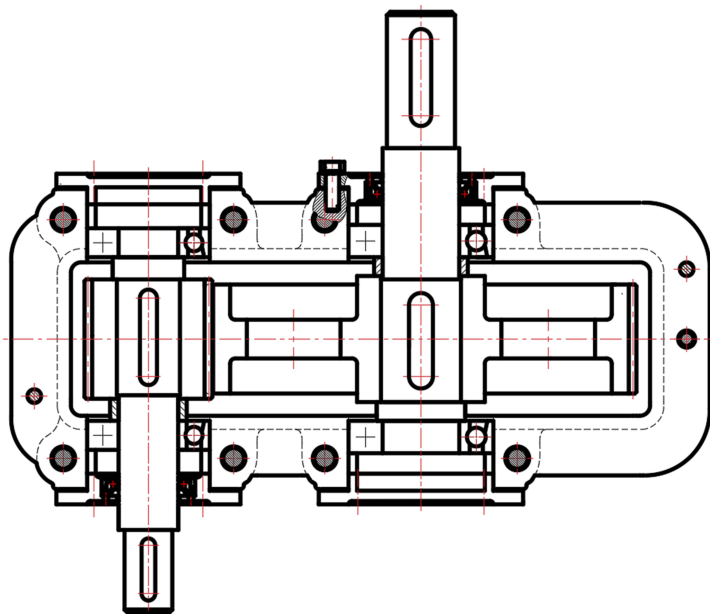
Изображение фундаментного фланца корпуса редуктора
